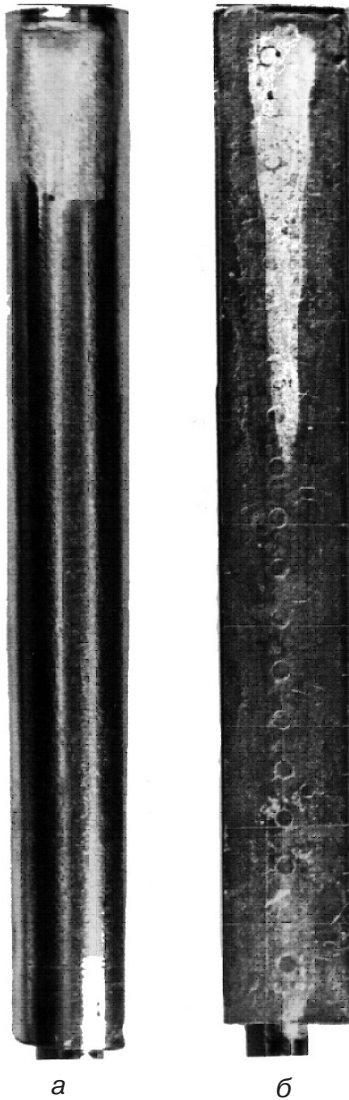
Внешний вид отливок из сплава Al+5,8%Si со стороны цилиндрической (а) и плоской (б) поверхностей; скорость заполнения формы – 7 см/с; температура заливки – 750 °С
